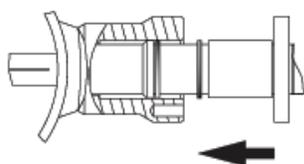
Насадочное кольцо, детальный чертеж
